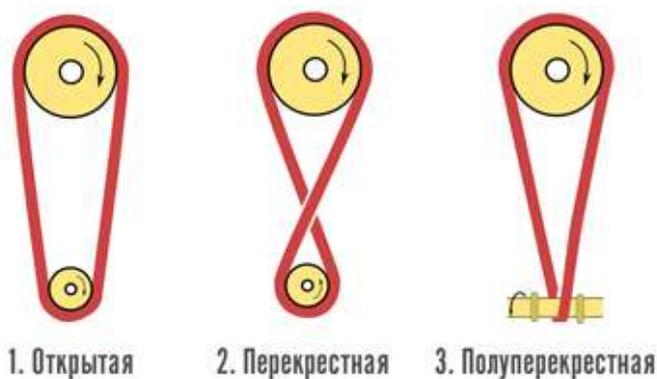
Открытая, перекрестная и полуперекрестная передача
